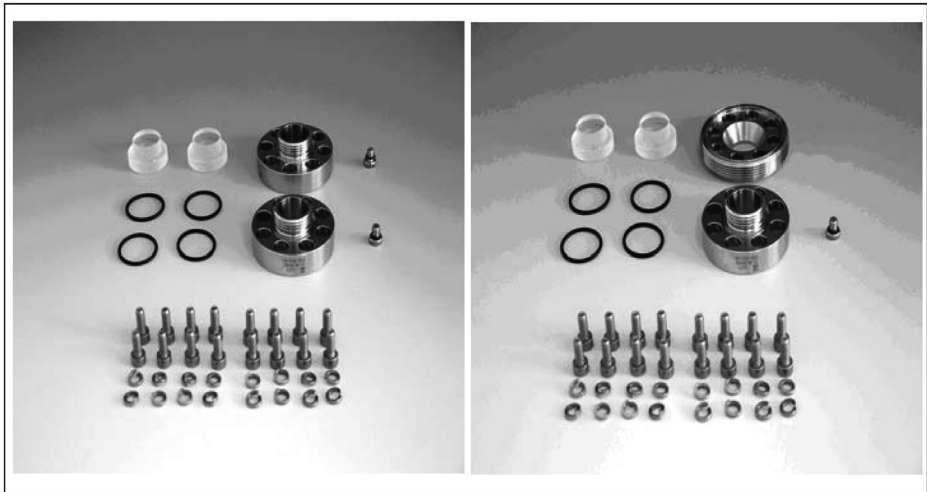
Parti necessarie per l'assemblaggio (Anelli dell'oblò, oblò, viti, rondelle e set di guarnizioni)
